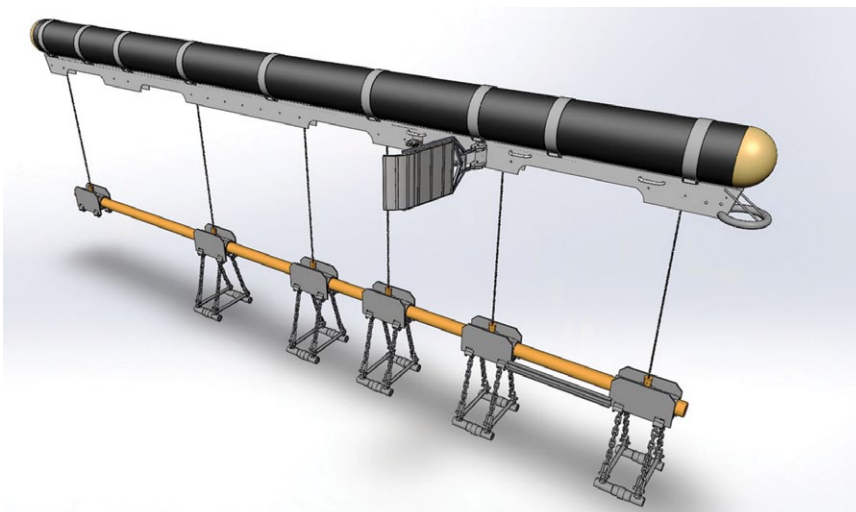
Общий вид конструкции паравана и подруливающего крыла
